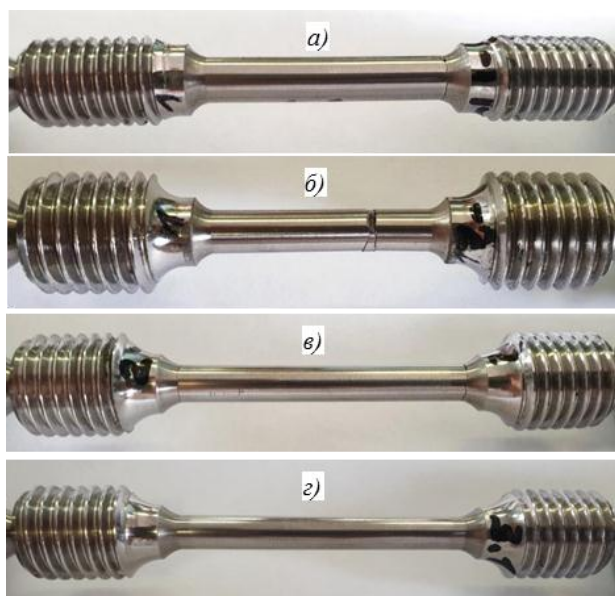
Характер разрушения образцов из подшипниковой стали:
